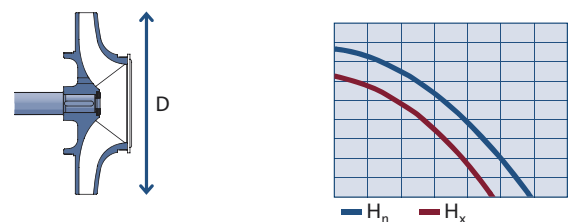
Anpassung des Laufraddurchmessers
